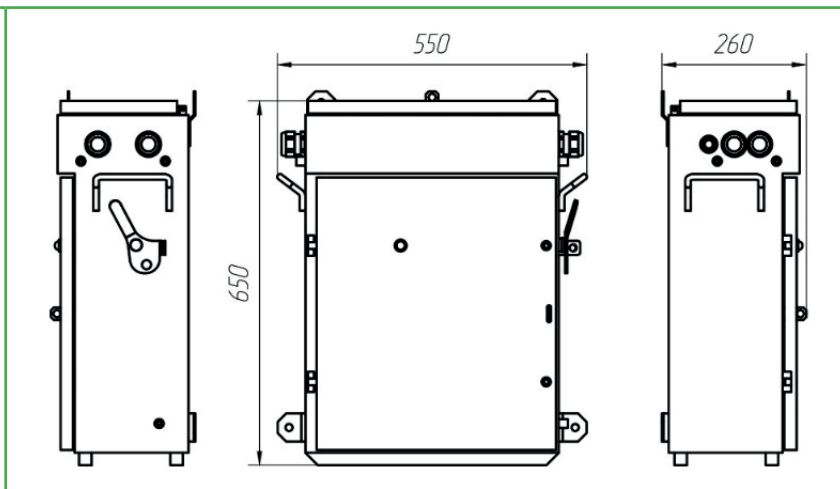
Конструкция АОШ-0,8(1,6)-3Ф-660-380/36
